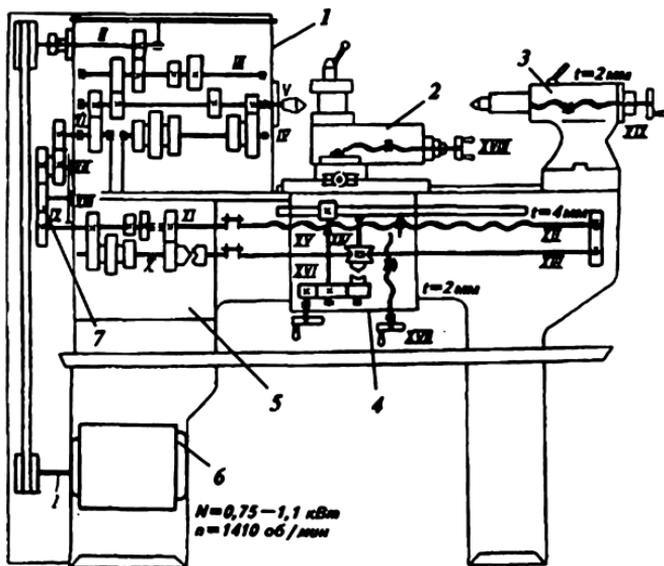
Кинематическая схема токарно-винторезного станка ТВ-6:
